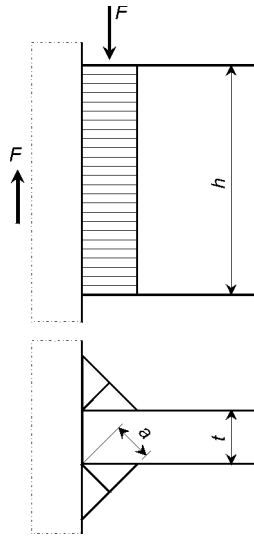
Unión con doble soldadura en ángulo cargada paralelamente al eje de soldadura
